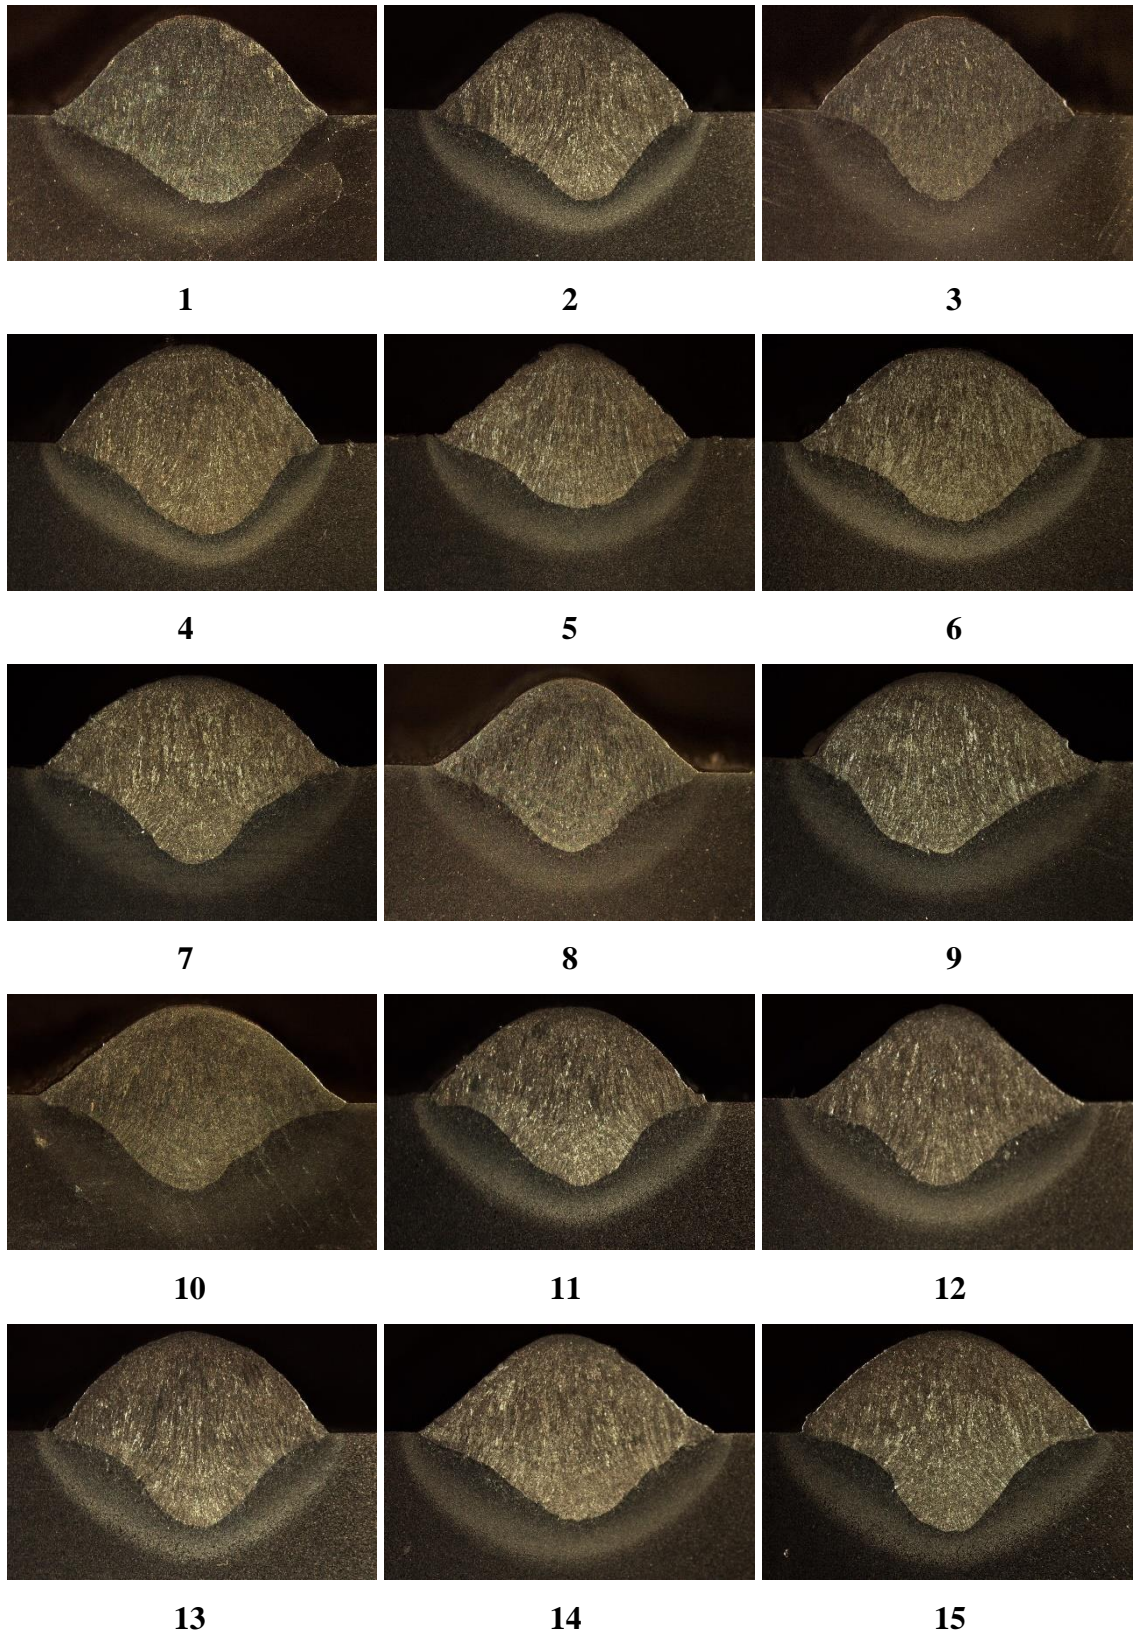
Macrografias dos cordões de solda MAG com arame de 1,2 mm de diâmetro.
